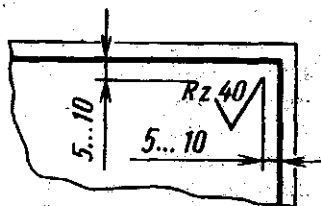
Обозначение шероховатости для всех поверхностей детали
